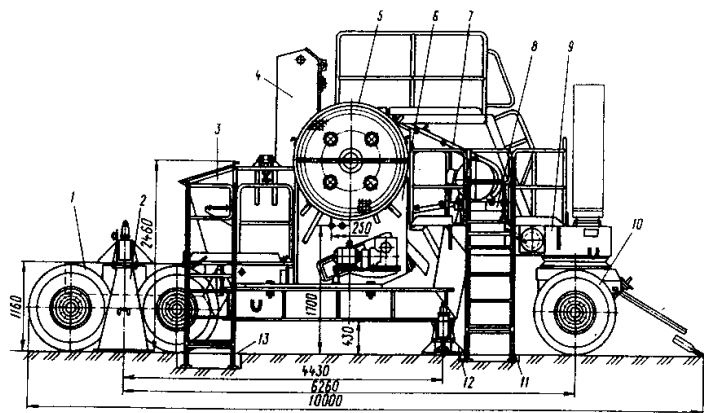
Агрегат крупного дробления СМД-133: 1 — тележка задняя; 2, 12 — опоры; 3 — течка; 4 — бункер загрузки; 5 — ограждение; 6 — дробилка; 7 — ограждение привода; 8 — привод дробилки; 9 — рама в сборе; 10 — тележка передняя; 11, 13 — лестницы
